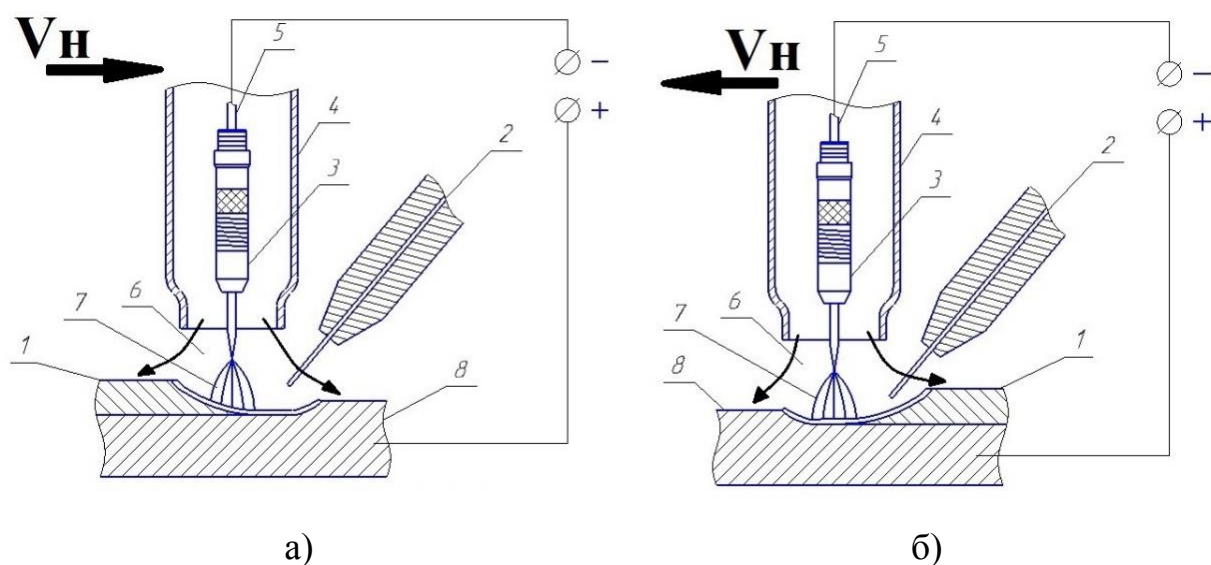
Схема процесса аргонодуговой наплавки неплавящимся электродом: а) левый способ наплавки (проволока подается в головную часть сварочной ванны) б) правый способ наплавки (проволока подается в хвостовую часть сварочной ванны)
